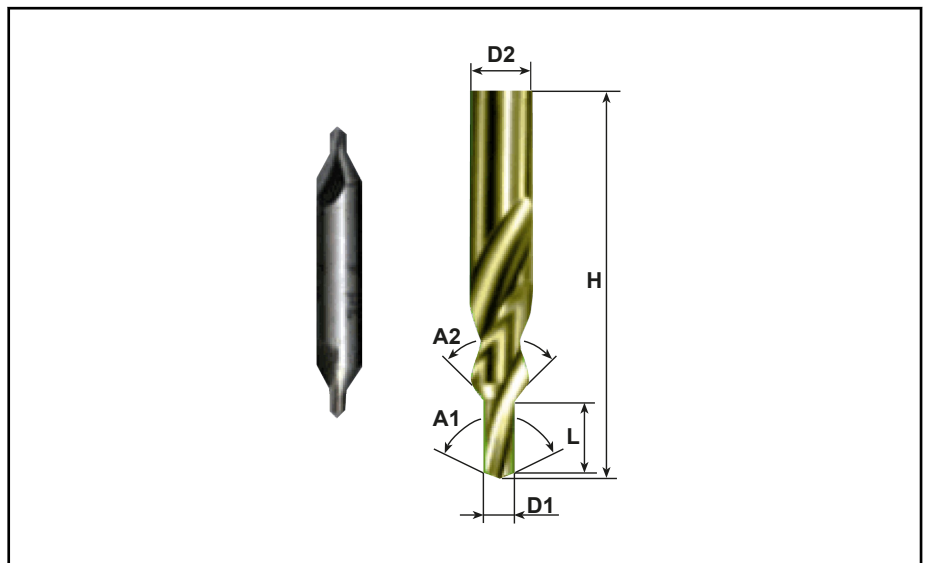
Werkzeugbeschreibung TOOL/CDRILL Stufenbohrer, Zentrierbohrer
